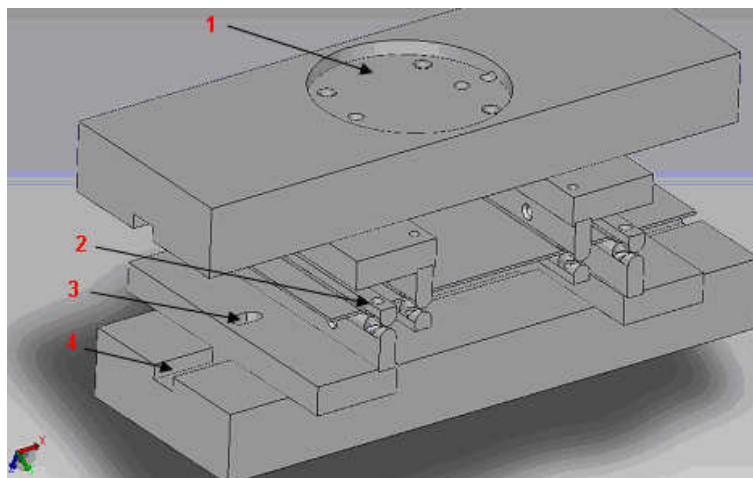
Design des appuis fabriqués pour être montés sur la machine de test de flexion
